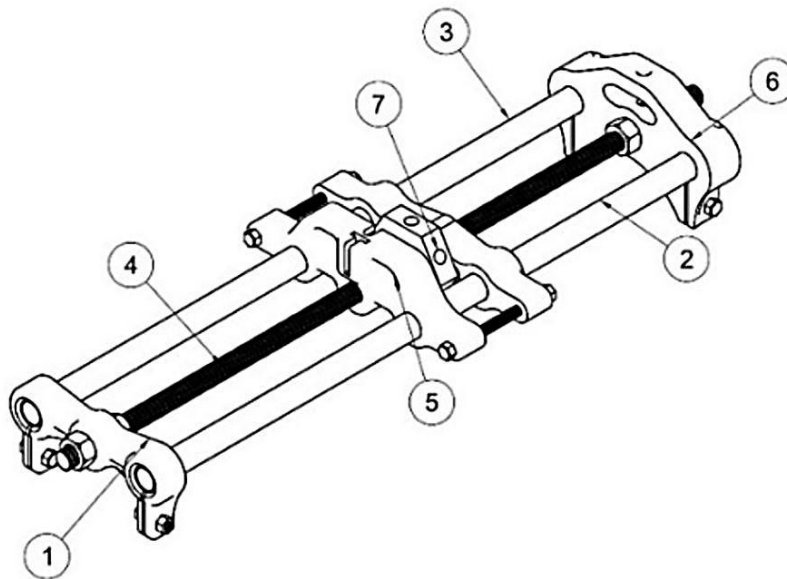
Общий вид станда: 1 – стойка; 2, 3 – направляющие; 4 – шпилька; 5 – каретка; 6 – стойка с креплением под измерительный прибор; 7 – колесо с гайкой
